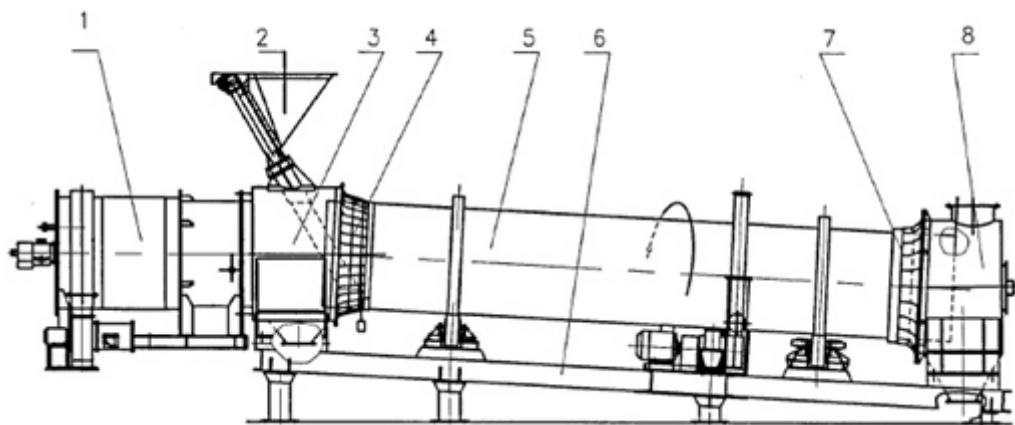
Сушильний агрегат барабанного типу:
